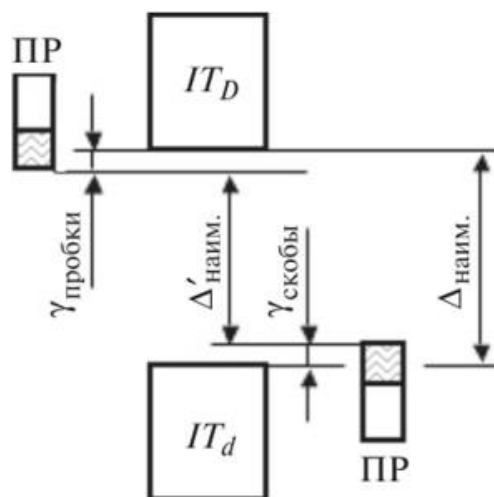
Схема полей допусков при контроле изношенными проходными калибрами
